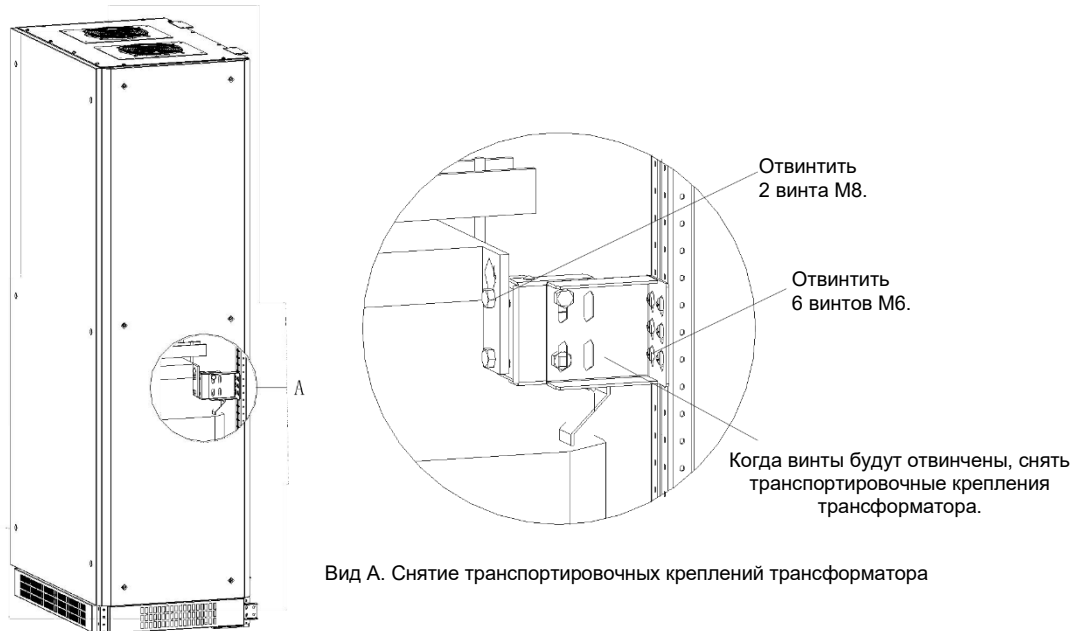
Снятие транспортировочных креплений фазорегулирующего трансформатора
